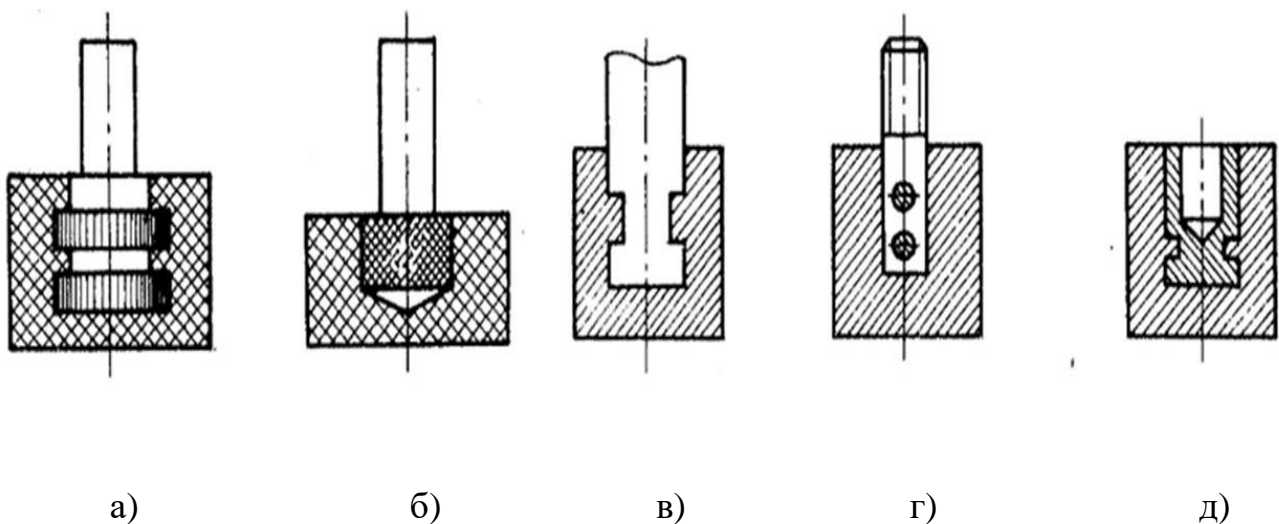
Приклади заформування: а, б – запобігання деталей від провертання за допомогою рифлень; в, г, д – заформування металевих деталей в метал
